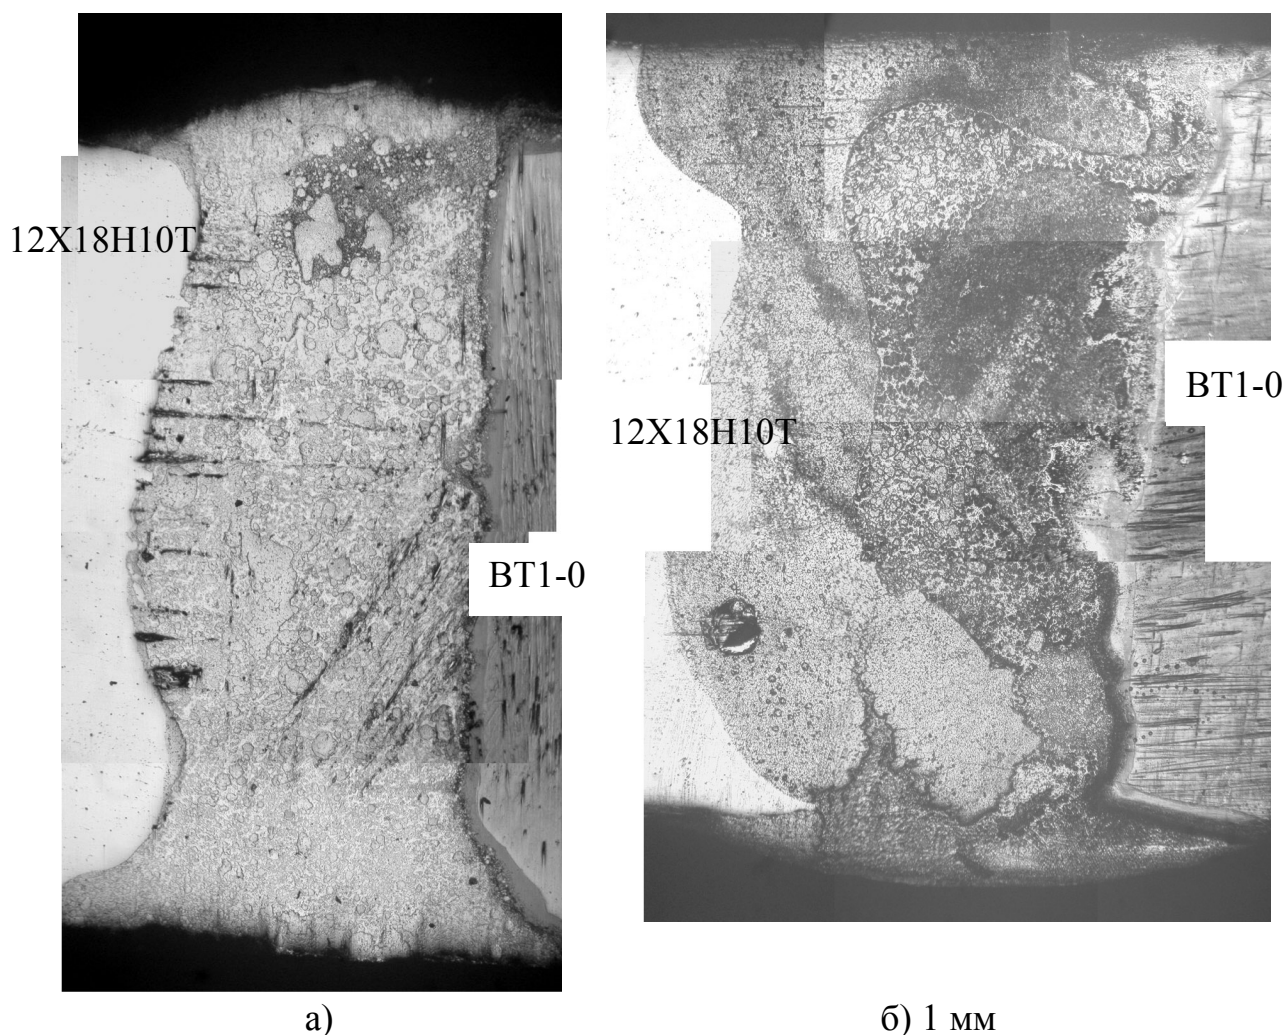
Макроструктура сварных соединений: *а)* – сварка по режиму 1; *б)* по режиму 6 (табл.)
